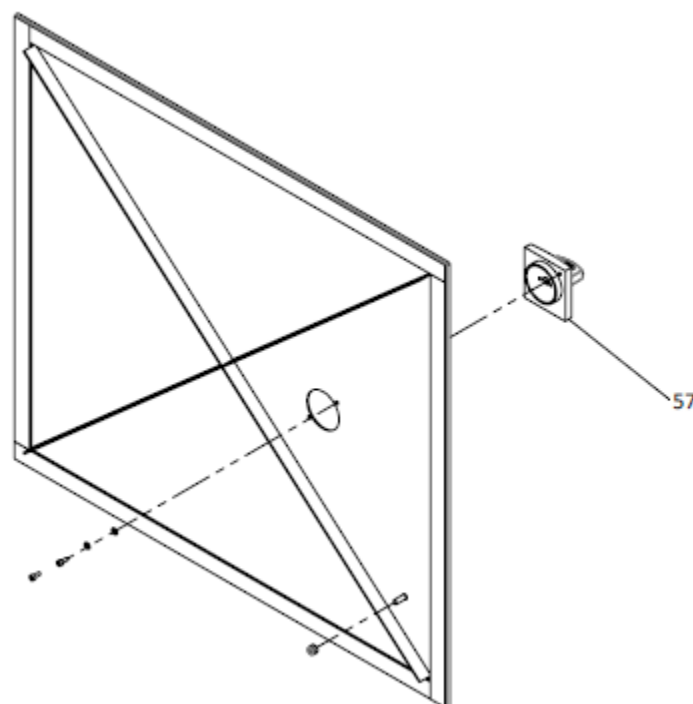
Рукоятка предохранителя перечня деталей НИП серии 2500+
